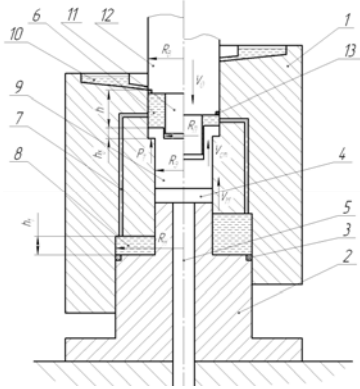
Схема штампів для видавлювання з розтягом сталевих виробів з порожниною постійного діаметра
